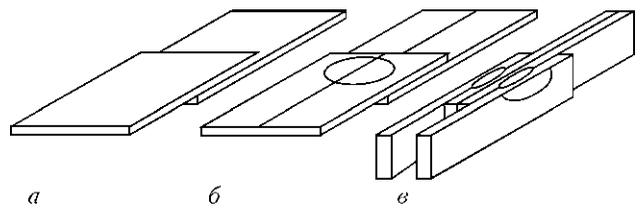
Схема подготовки сварных образцов к изготовлению микрошлифов: а — перед сваркой; б — после сварки с линейной разрезом вдоль сварной точки; в — для изготовления микрошлифа
